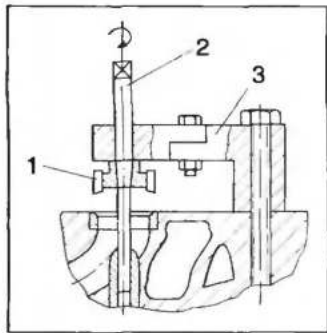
Схема приспособления для ручного растачивания седла или его гнезда:
